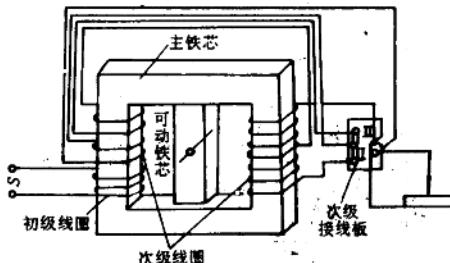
4 BX1 - 330 型弧焊变压器的结构原理图
